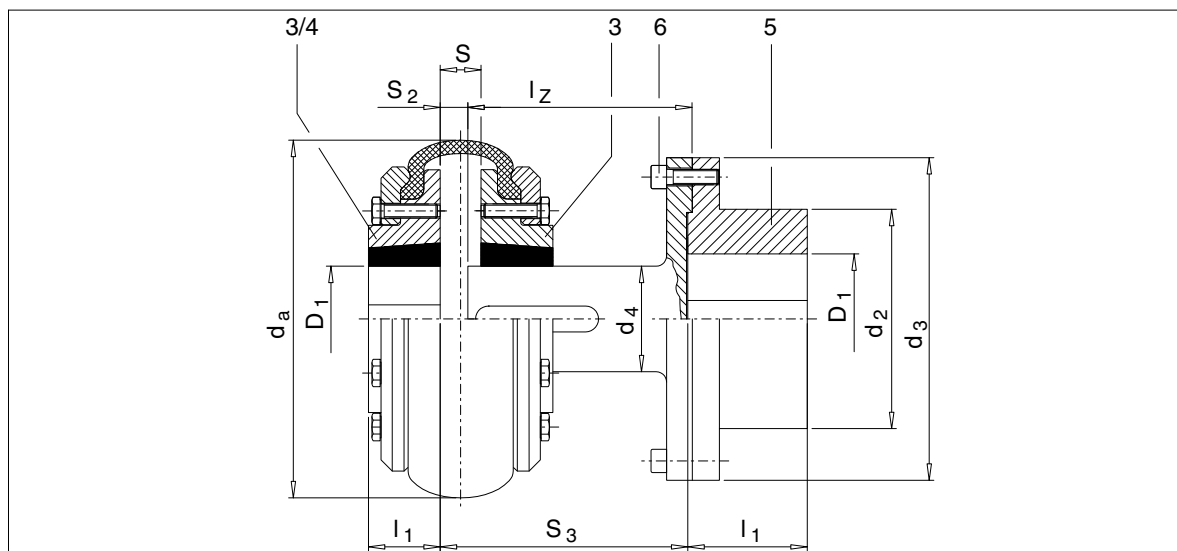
Чертеж с размерами типа EBWZ, размеры 105 до 360
